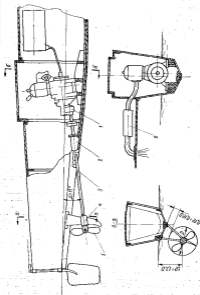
Установка двигателя в корпус катамарана. 1 — двигатель; 2 — пропеллер; 3 — ступица; 4 — корпус; 5 — вал.
